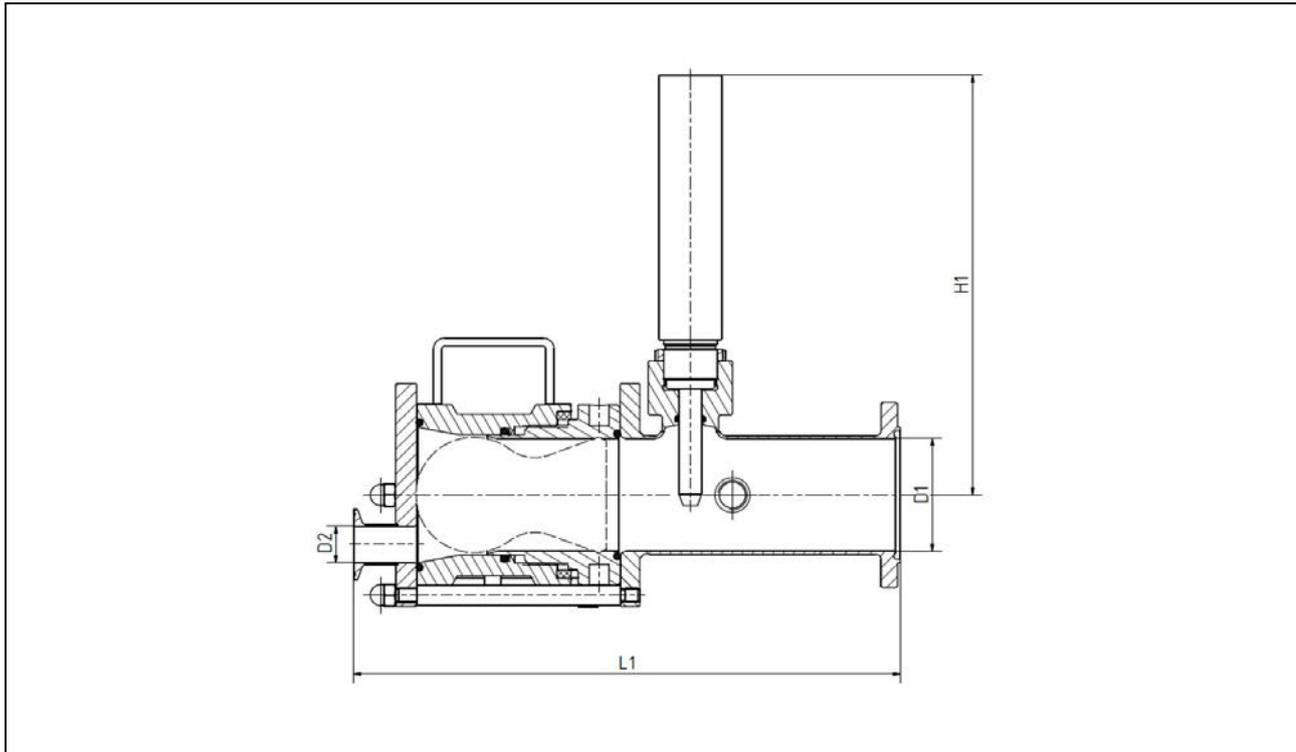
Steckkammer mit Stopper, Anschlussvariante Zoll, Serie D
